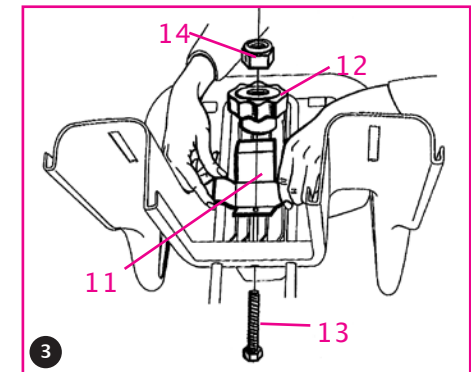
Schließlich die selbstsichernde Mutter (14) einschrauben.
